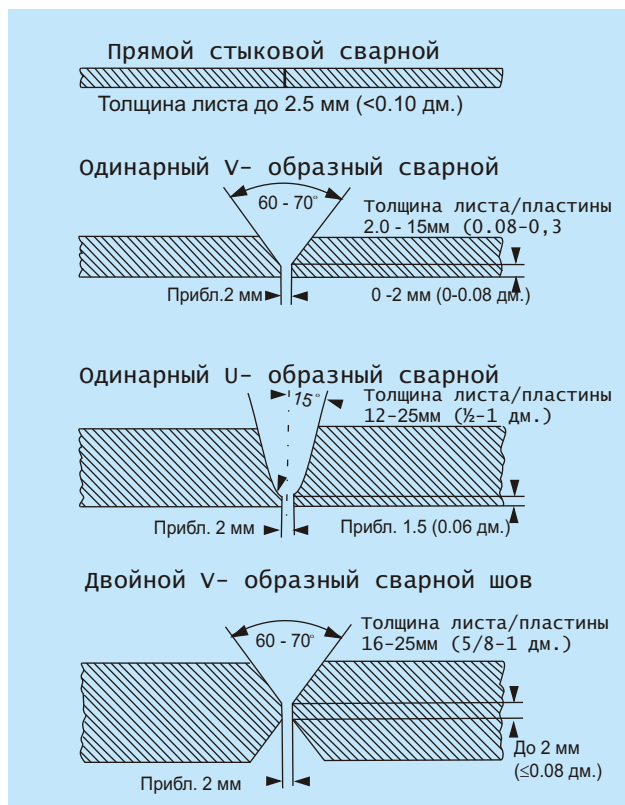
Подготовка кромок для сваривания никелевых сплавов и специальной нержавеющей стали
